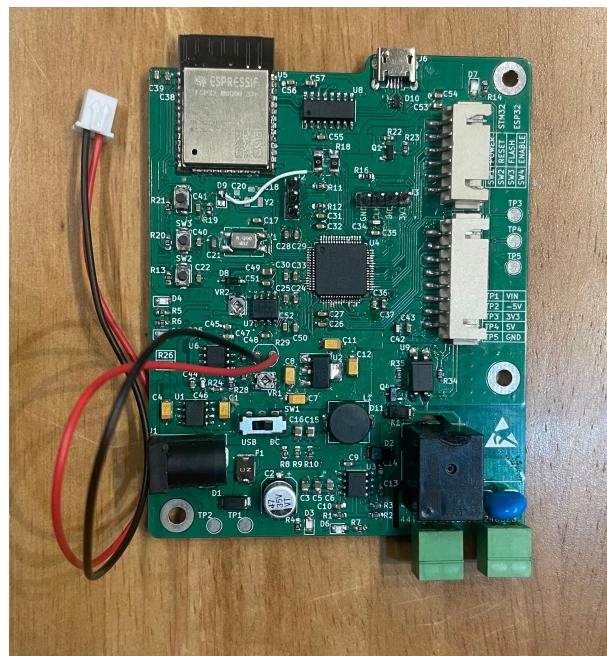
Hình ảnh thiết kế mặt trên của PCB
